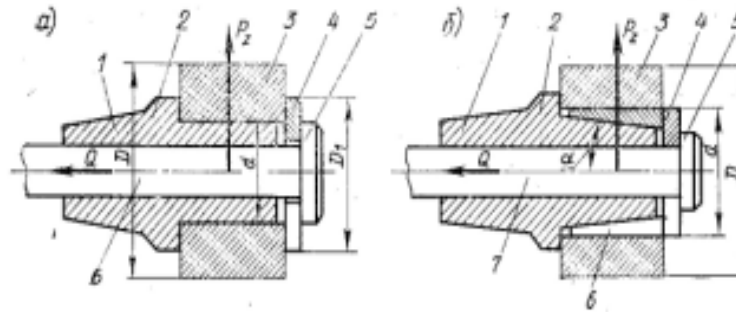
Конструкції оправок: а - гладка оправка; б- оправка з розрізною втулкою
